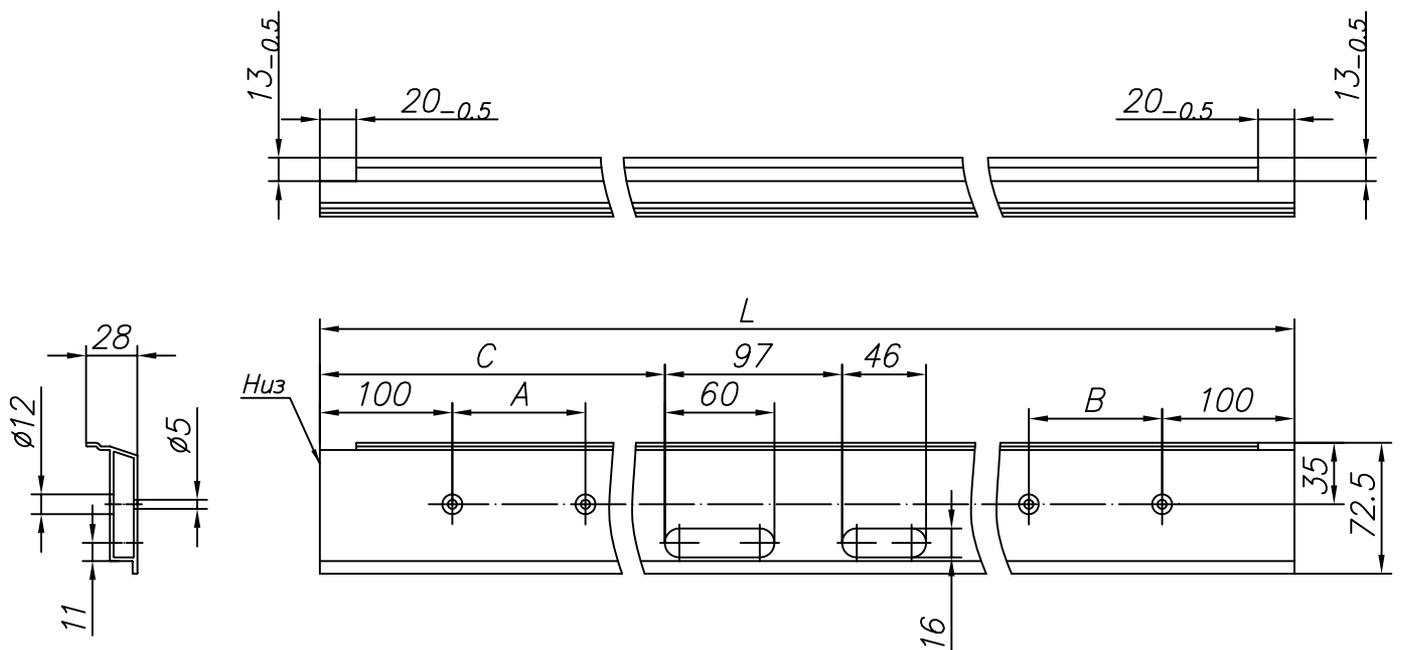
Изготовление притвора с пазом для ответной пластины замка из профиля FLGU.400.0505 (открытие внутрь, влево)
